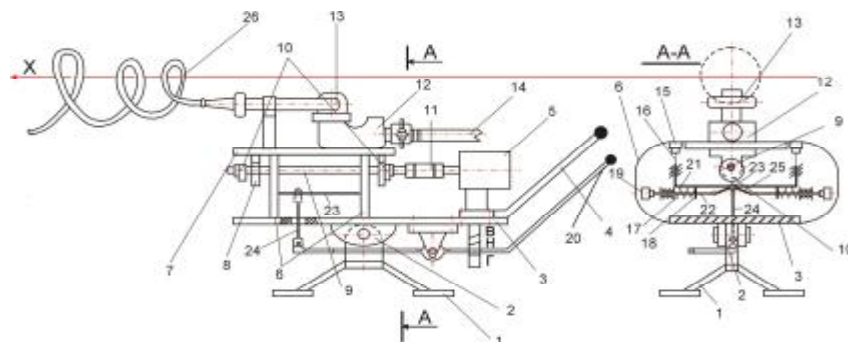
Конструктивно-кінематична схема лафетного вібраційного ствола: 1 - опорна основа; 2 - шарнірне з'єднання; 3 - нерухома основа вібраційного стола; 4 - ручка керування; 5 - привід обертового руху; 6 - ресорна підвіска рухомої частини вібраційного стола; 7 - верхня частина стола, яка вібрує; 8 - підшипникові опори валу дисбалансів; 9 - вал дисбалансів; 10 - дисбаланси; 11 - еластична муфта; 12 - приймальний корпус; 13 - ствол; 14 - напірний патрубок; 15 – притискна подушка (вертикальна); 16 – гнучка пластина; 17 – пружина; 18 – упорна шайба; 19 - притискна подушка (горизонтальна); 20 – ручка перемикач; 21 – коромисло; 22 – шток; 23 – вісь приводу тяг; 24 – вертикальна тяга; 25 – штовхач; 26 – коловозвинтовий або еліпсогвинтовий компактний струмінь рідини.
